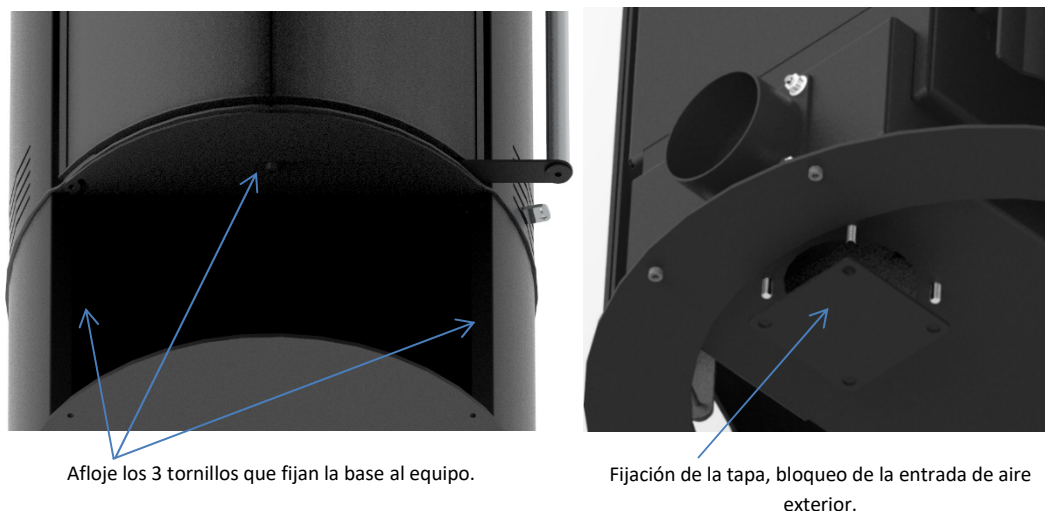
Vista inferior del equipo, bloqueo de la entrada de aire externa debajo del equipo
